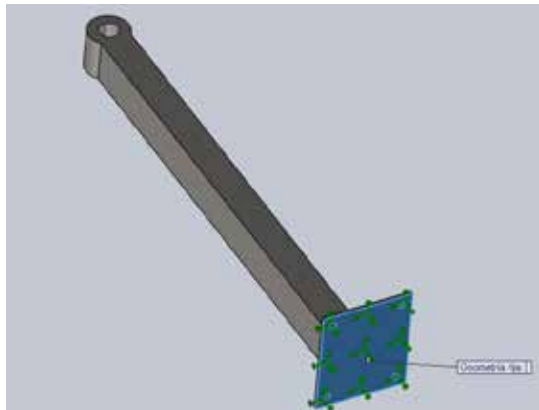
Sujeciones aplicadas a la Estructura de Apoyo
